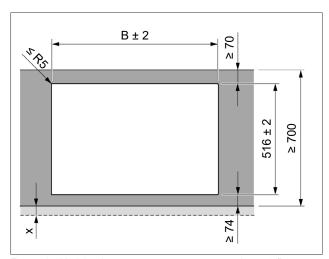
Medidas de recorte para montagem por sobreposição
